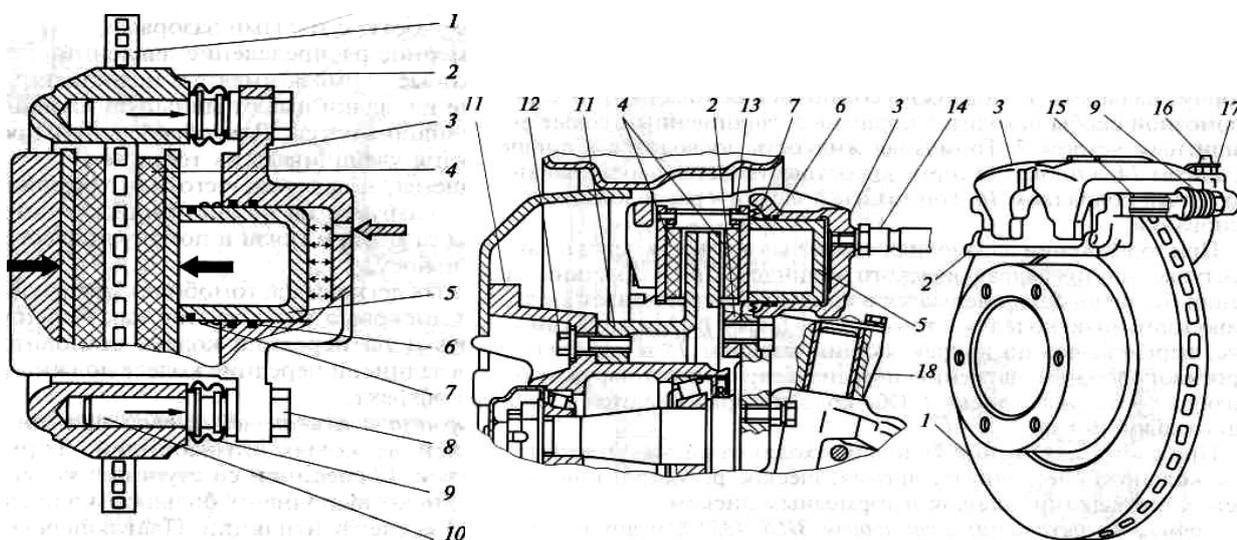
Передний дисковый тормозной механизм: 1-тормозной диск; 2 — основание тормозной скобы; 3 — корпус тормозной скобы; 4 — поршень; 5 — уплотнительное кольцо; 6 — защитные чехлы; 7, 9 — направляющий палец; 8, 12 — болты; 10 — направляющий палец; 11 — ступица колеса; 13 — пружина колодки; 14 — колпачок; 15 — направляющий палец; 16 — клапан прокачки; 17 — поворотный кулак; 18 — поворотный кулак
